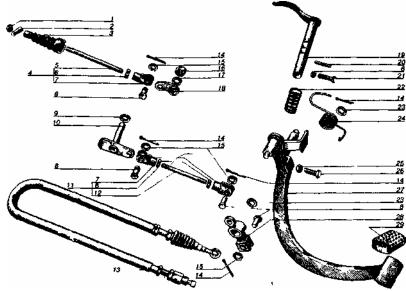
Привод тормозов мотоцикла "Днепр-11/16": 1 - гайка специальная; 2 - ось рычага; 3 - муфта; 4 - тяга задняя в сборе; 5 - тяга задняя; 6, 16, 26 - гайки; 7 - вилка тяги; 8 - палец; 9 - втулка; 10 - рычаг промежуточный; 11 - тяга передняя в сборе; 12 - тяга передняя; 13 - трос тормоза колеса коляски; 14 - шплинт; 15, 17, 23 - шайбы; 18 - рычаг внутренний; 19 - рукоятка стояночного тормоза; 20 - штифт; 21, 25 - болты; 22 - пружина; 24 - пружина возвратная; 27 - рычаг ножной в сборе; 28 - уравниватель тормоза; 29 - накладка
